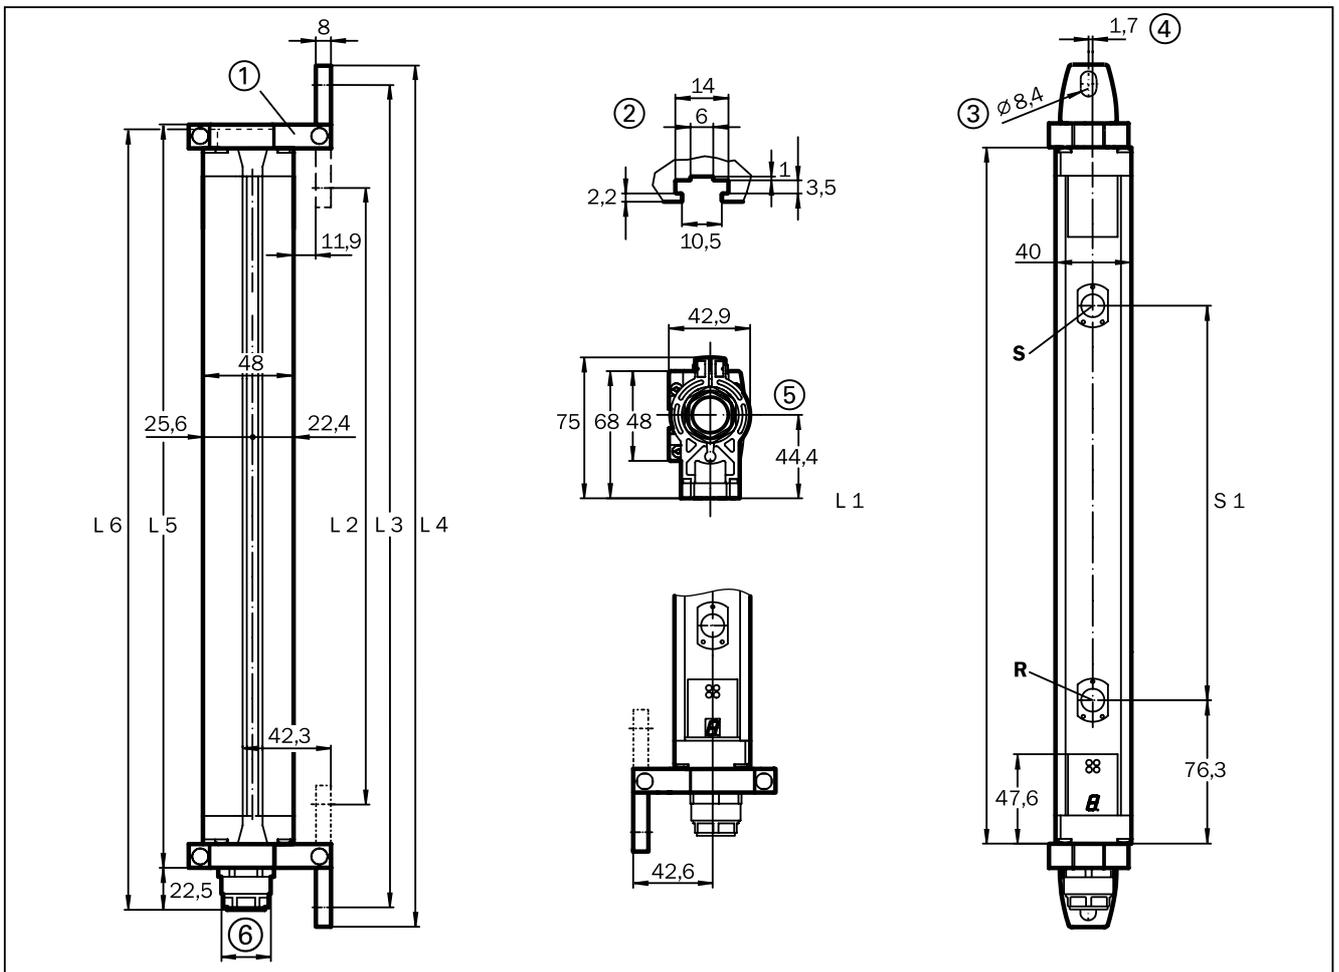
Plans et cotes d'encombrement M 2000-A/P, montage sur rotules
